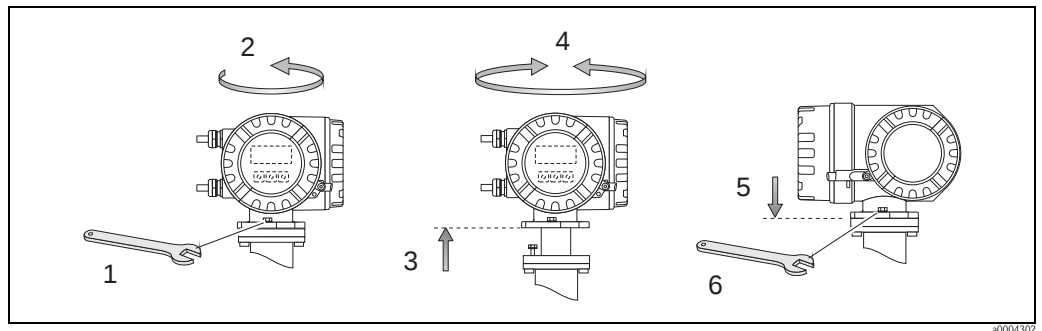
Drehen des Messumformergehäuses (Aluminium-Feldgehäuse)
